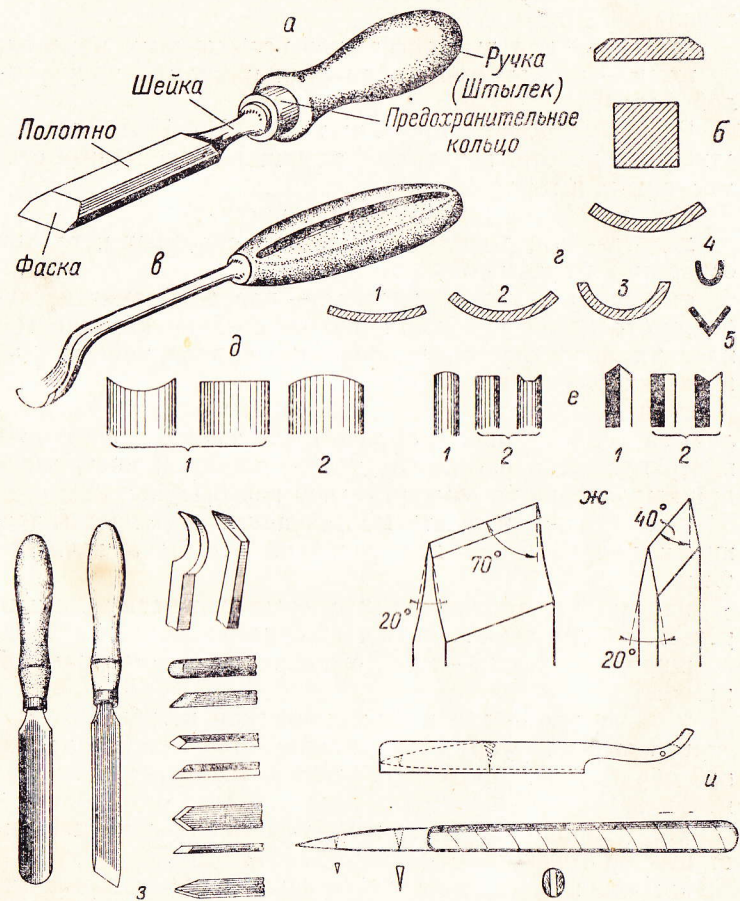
Режущий инструмент: а — стамеска (схема); б — сечения полотна стамески (вверху), долота и полукруглой стамески (внизу); в — клюкарза; г — сечения полотен резчицких стамесок: 1 — пологой; 2 — средней; 3 — кругой; 4 — царзика; 5 — уголка; д — форма лезвия полукруглой резчицкой стамески: 1 — неправильно; 2 — правильно; е — форма лезвия царзика и уголка: 1 — неправильно; 2 — правильно; ж — токарные резцы: рейер (слева), косяк, грабштихели и крючки; з — форма лезвия широкого (слева) и узкого резачок; и — нож для маркетри из старой бритвы.
